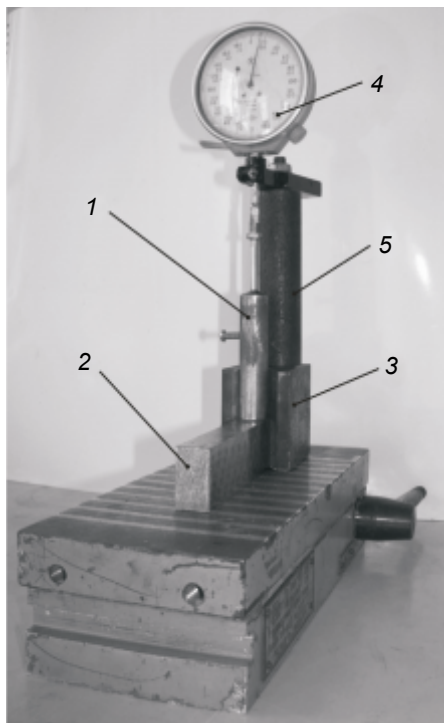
Фотография измерительного приспособления для определения величины износа корундового образца
